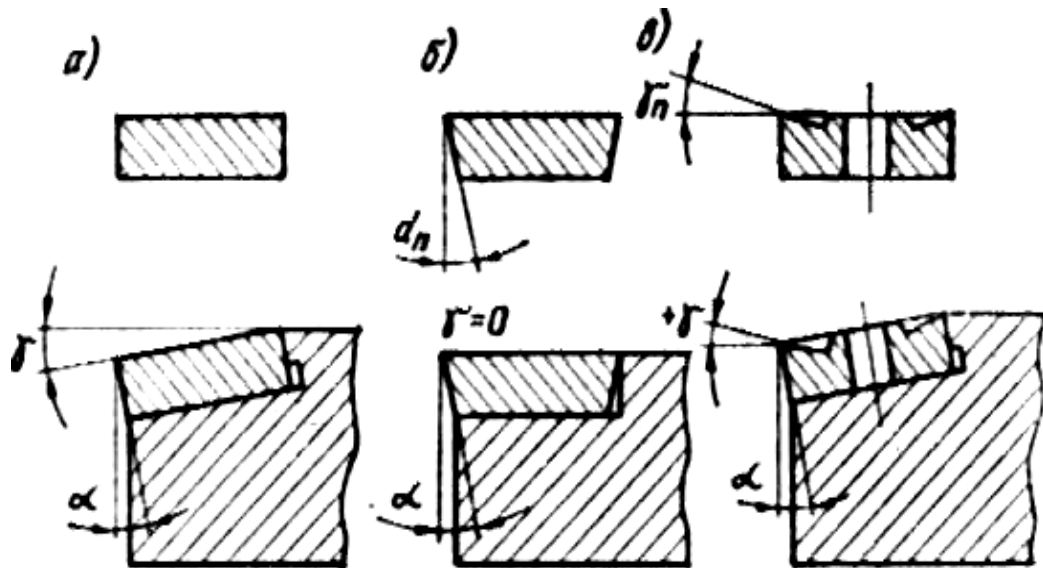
Схеми установки багатограних непереточуваних твердосплавних пластин в утримувачі різця
